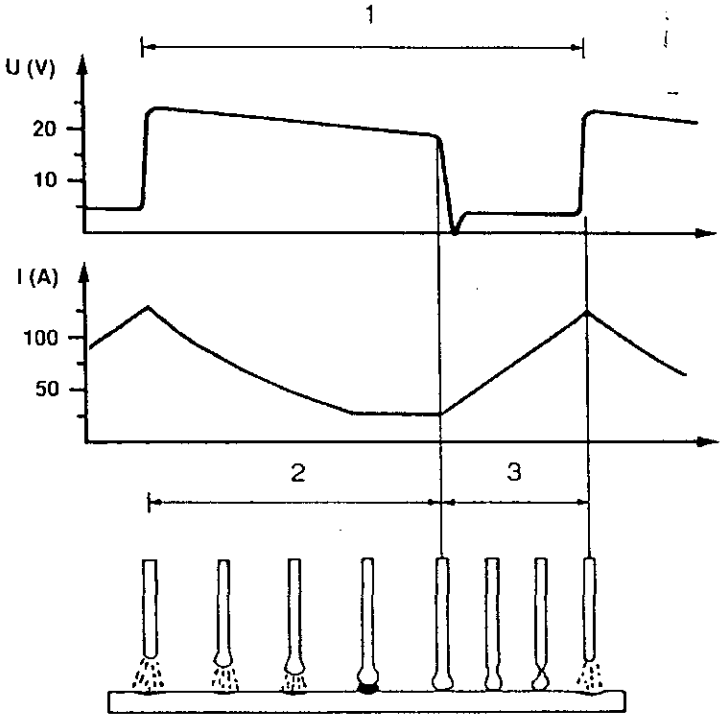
Proceso de deposición de la soldadura
